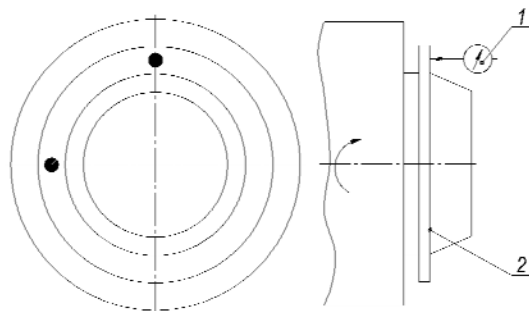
Схема перевірки геометричної точності розташування торцевої поверхні шпинделя
